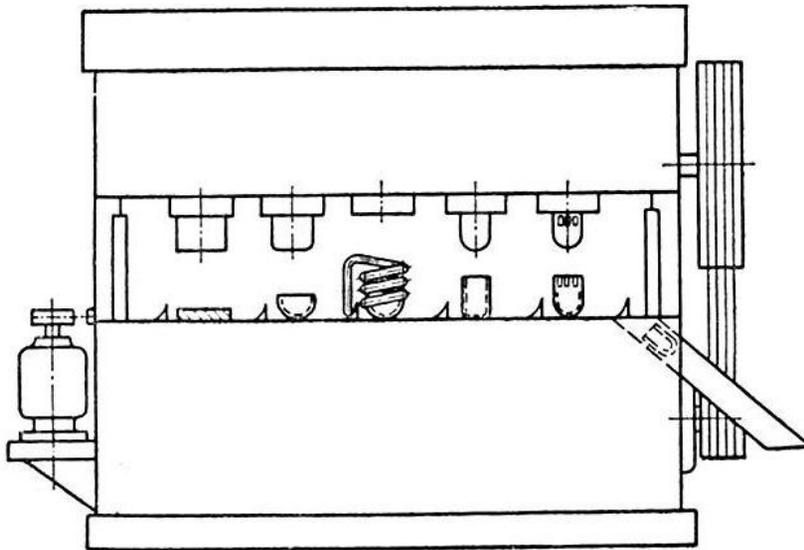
Многопозиционный пресс для штамповки колпачков
